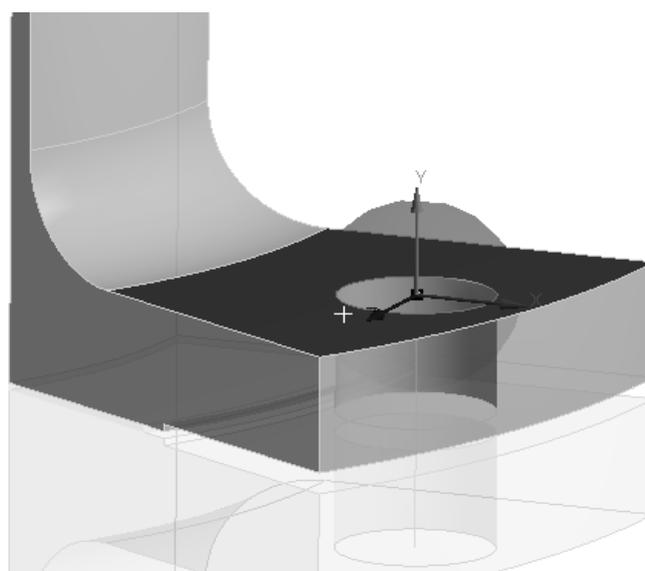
Соединение вершины балочного элемента с гранью верхнего фланца шарниром
